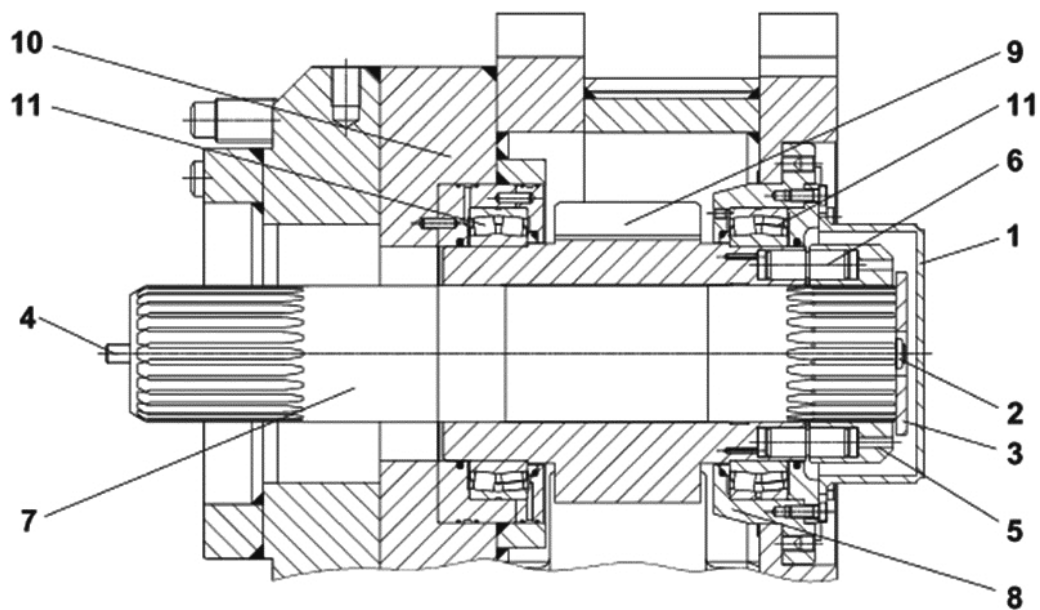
Узел приводного вала цевочно-реечного механизма подачи
